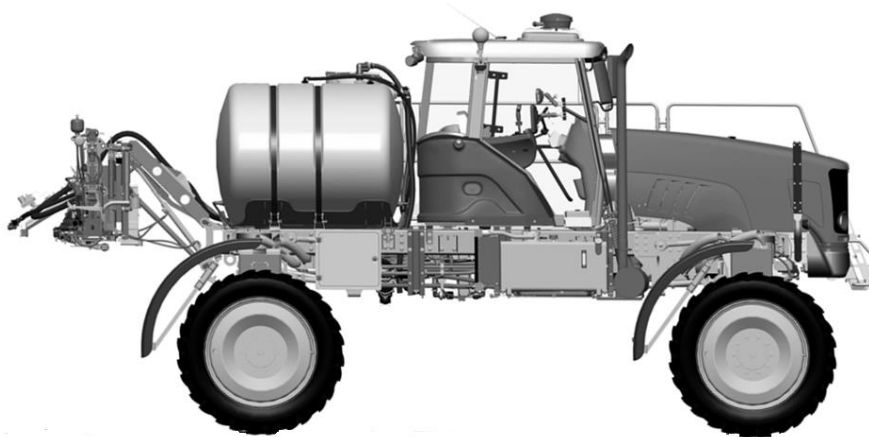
Pulverizador com cabine posicionada no centro da máquina, motor frontal, barras e reservatório de calda traseiros.
